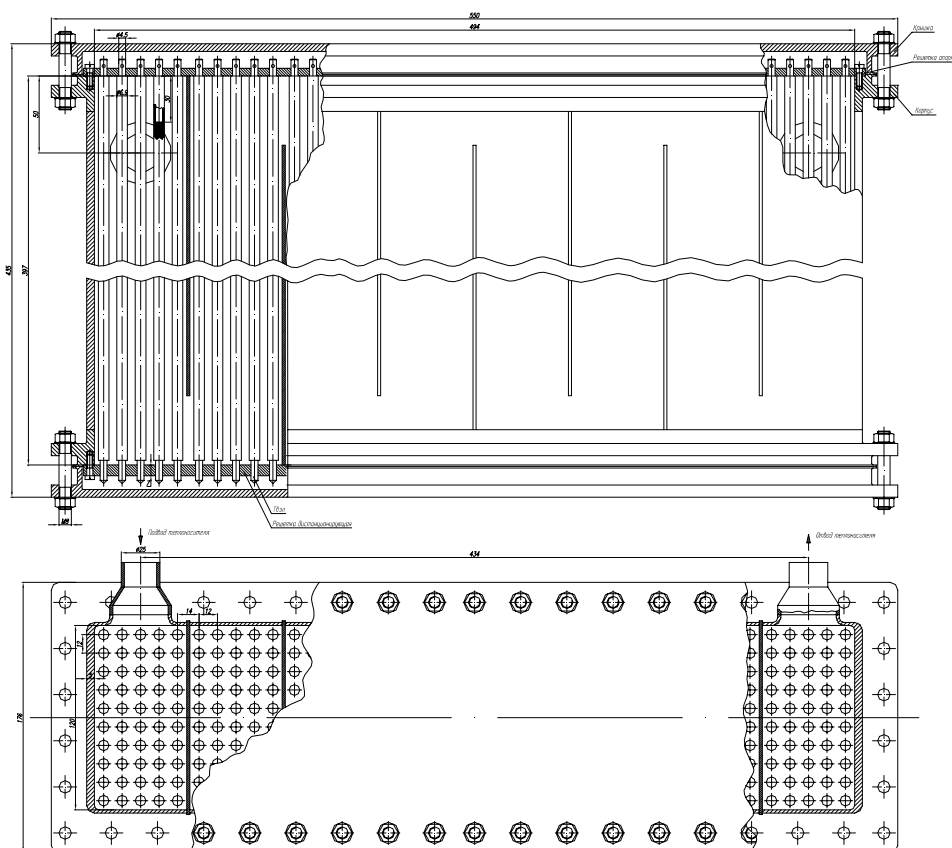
Конструкция корпуса реактора РУ МАРС с установленными твэлами
